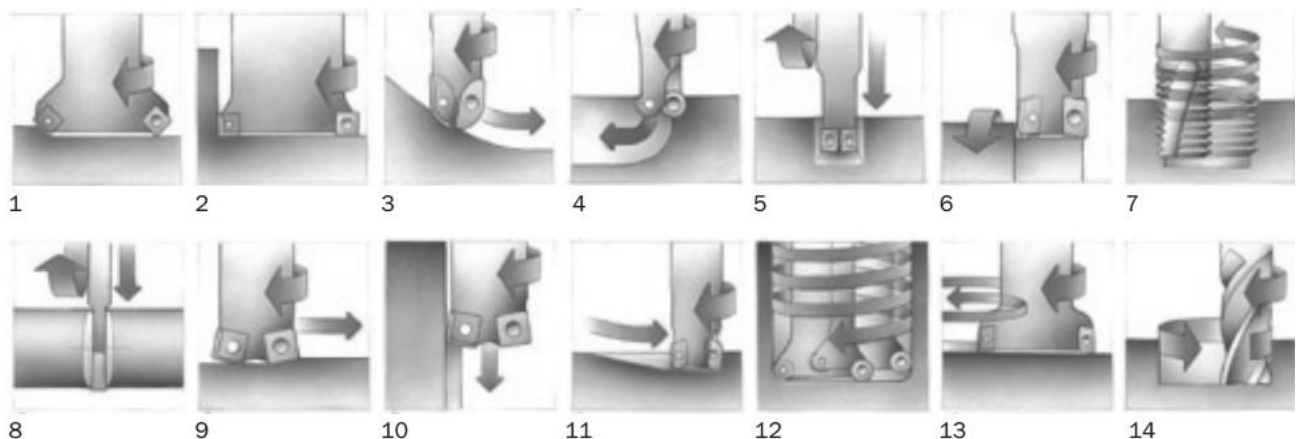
Основні типи фрезерних операцій з точки зору форми оброблюваної поверхні і способу переміщення інструменту:
